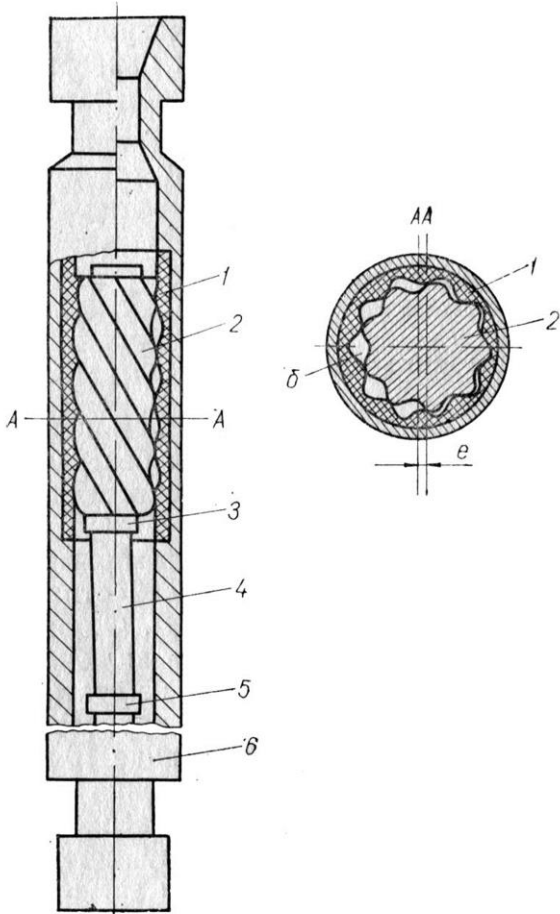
Схематичний розріз гвинтового двигуна:
